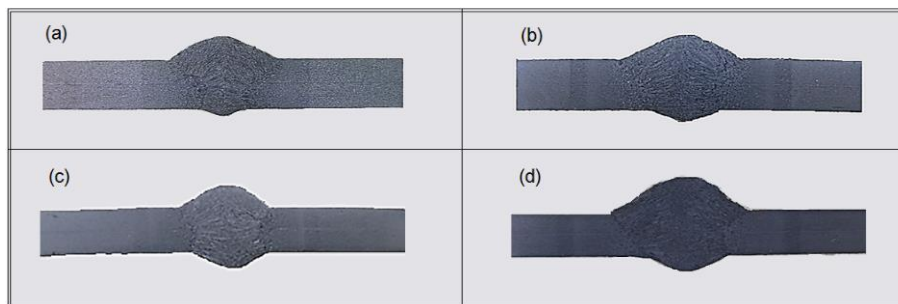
Fotomicrografias das juntas soldadas nos diferentes conjuntos de amostras de metal de base com metal de solda; (a) no aço ASTM A36 com arame-eletrodo AWS ER70S-6 (conjunto A1), (b) no aço ASTM A36 com arame-eletrodo AWS ER70S-3 (conjunto A2), (c) no aço CSN Civil-300 com arame-eletrodo AWS ER70S-6 (conjunto B1) e (d) no aço CSN Civil-300 com arame-eletrodo AWS ER70S-3 (conjunto B2)
